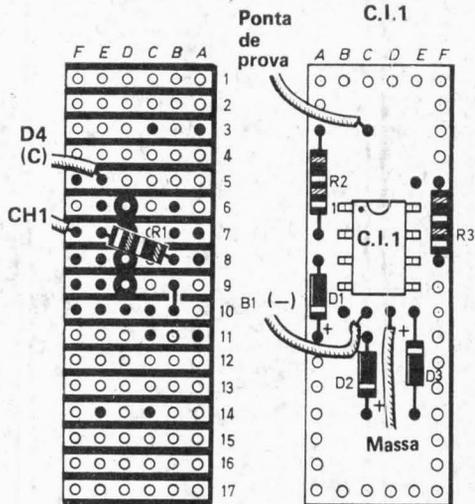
Plaqueta de circuito impresso universal utilizada na montagem do circuito da Fig. 1, e a disposição dos componentes. Observe que R1 é instalado na face cobreada da plaqueta. Os cortes dos filetes são apenas em número de 4. Sobre as ligações de C.I.1, ver legenda da Fig. 1.
